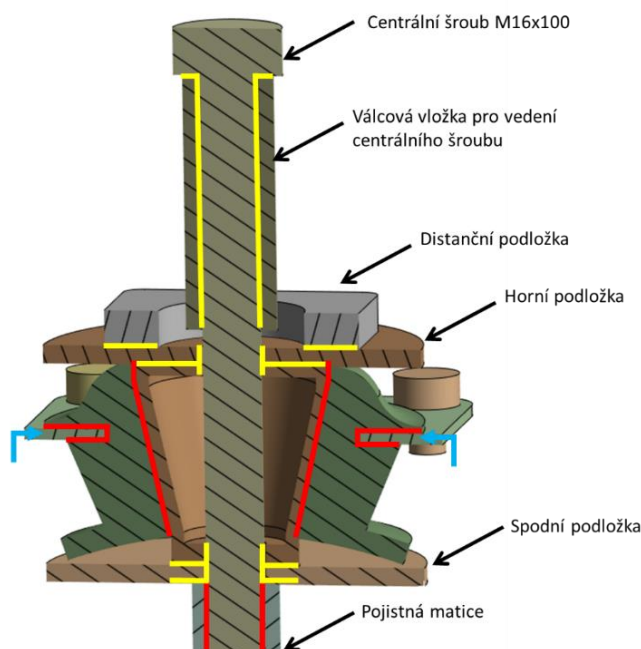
Šroubový spoj mezi vložkou silentbloku a konzolí předního systému odpružení.
